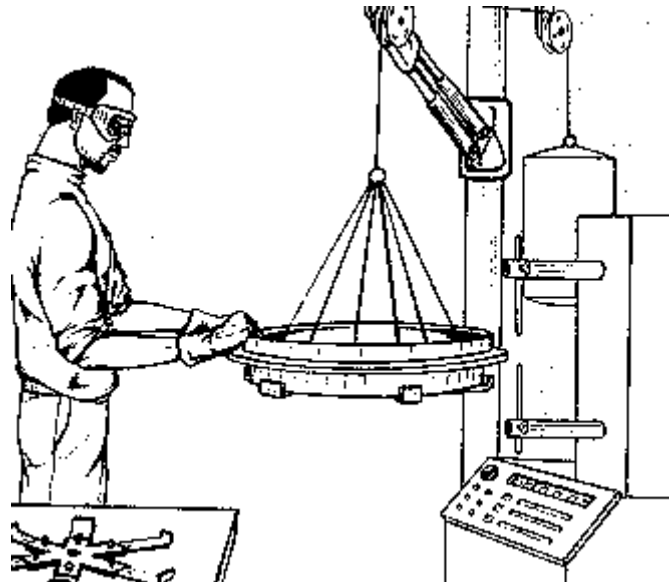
б. Балансировочные механизмы можно использовать также для снижения веса, как инструмента, так и заготовки.
